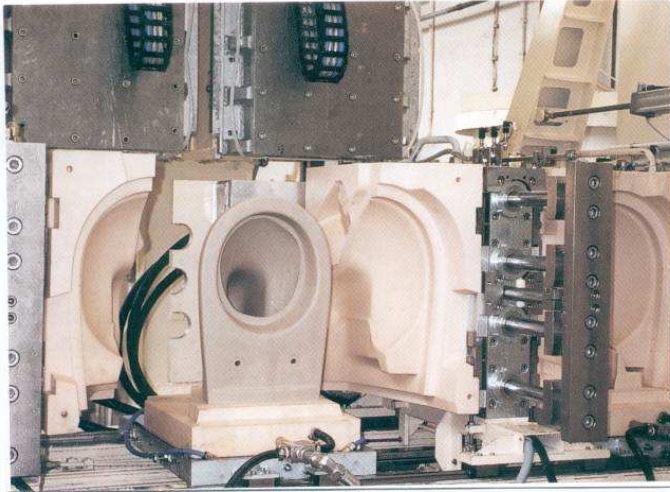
Druckgusswerkzeug für die WC-Fertigung.³¹
